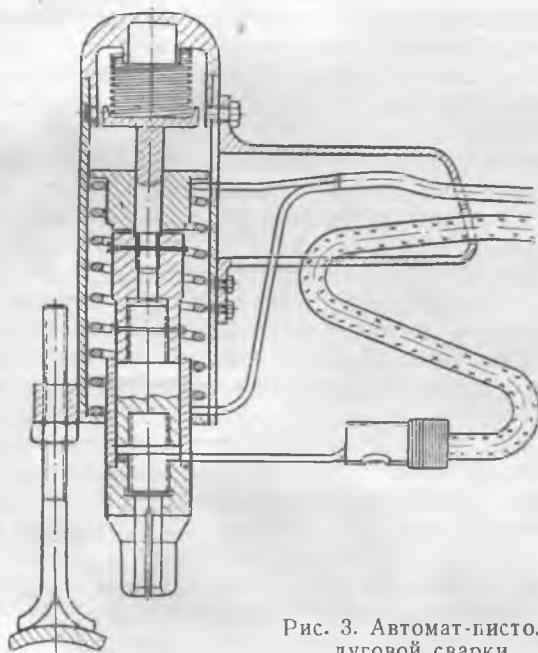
Автомат-пистолет дуговой сварки.
